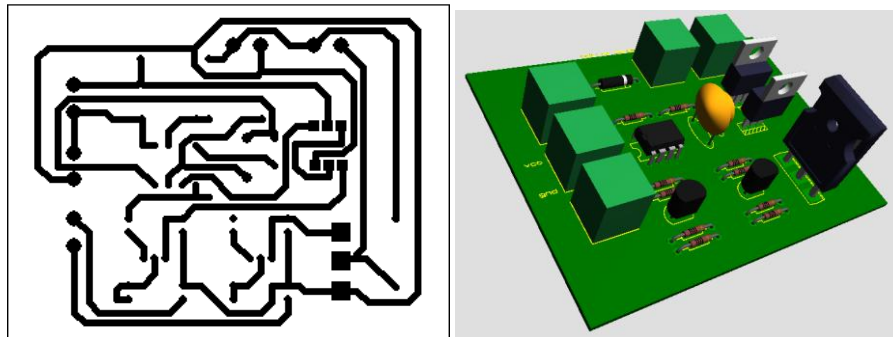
Circuito de pateo (a) PCB (b) Representación CAD
